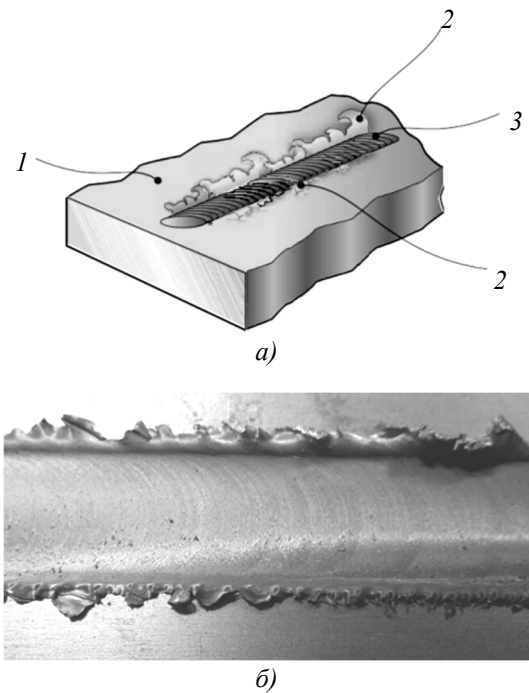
Схема (а) и вид (б) ($\times 2,5$) лицевой поверхности шва с дефектом типа графа, выполненного СТП на алюминиевом сплаве 1565чМ толщиной 5 мм: 1 – свариваемая заготовка; 2 – грат на стороне отхода инструмента; 3 – шов
